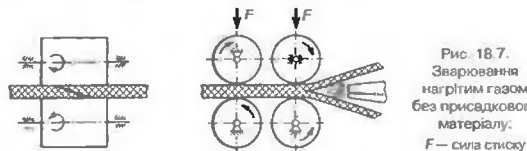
Зварювання нагрітим газом без присадкового матеріалу.
